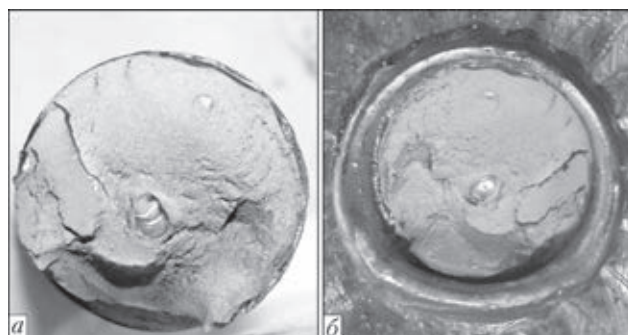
Внутренние дефекты сварки в образце № 3 первой серии: а — поры; б — несплавления
